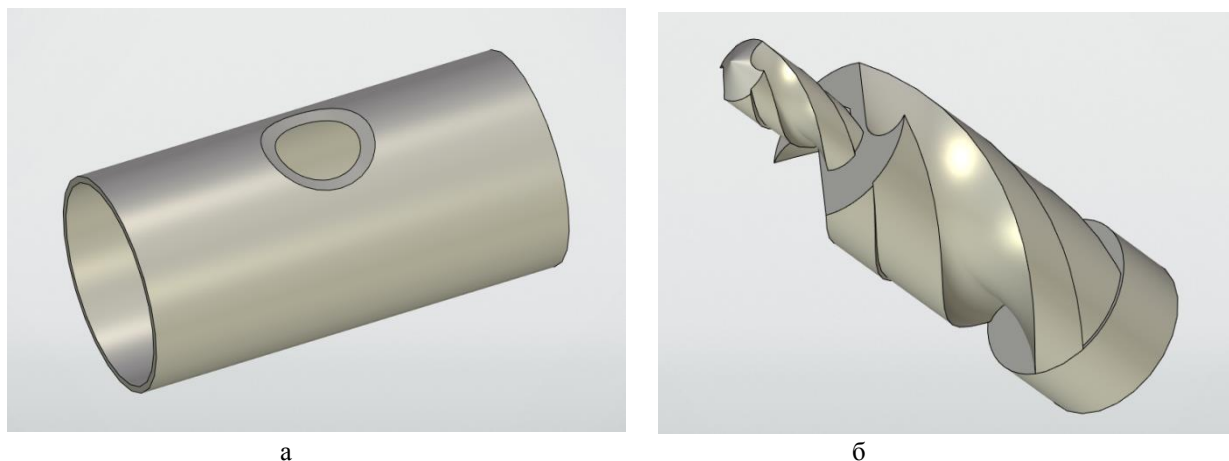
Напуск по контуру отверстия (а) и предлагаемая ступенчатая концевая фреза (б) для его обрезки
